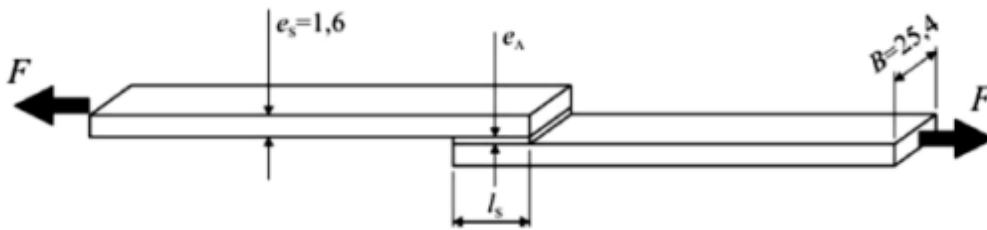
Geometria do ensaio JSS, segundo a norma ASTM D1002 (dimensões em mm) [55]
